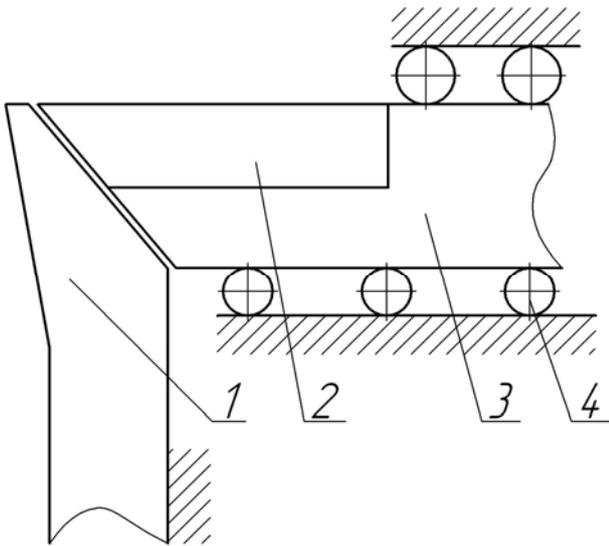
Режущая часть устройства для измерения сил трения и длин контактов
